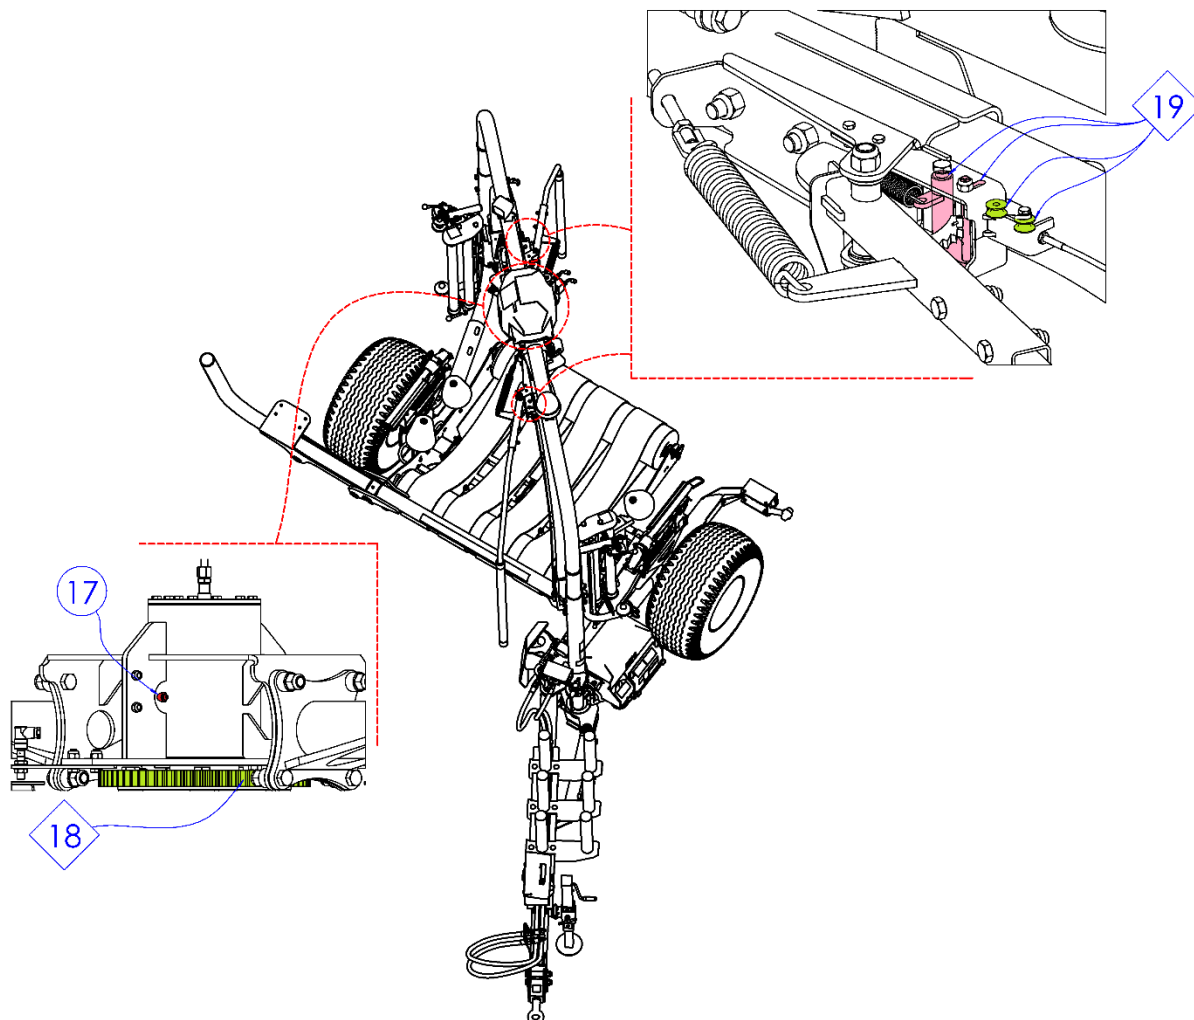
Точки смазки приводного модуля и защелок бамперов:
